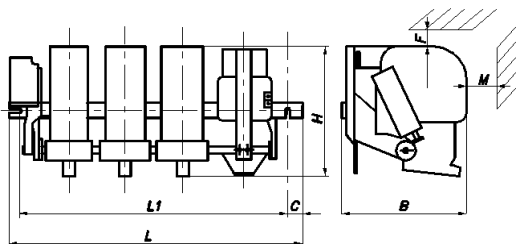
Общий вид и габаритные размеры КТ-6000.
